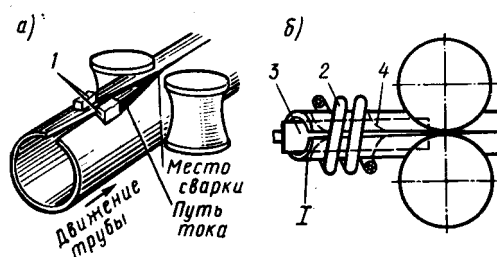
Схема контактной сварки труб токами высокой частоты:
